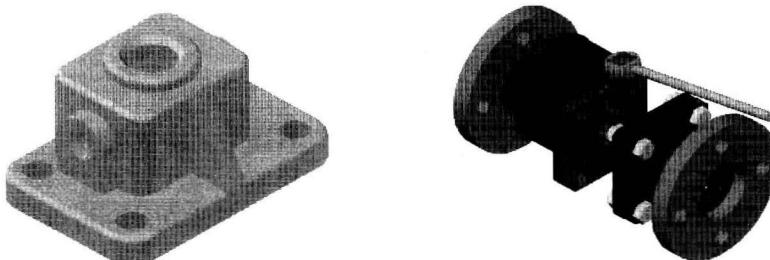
使用 AutoCAD 绘制三维零件图和装配图
